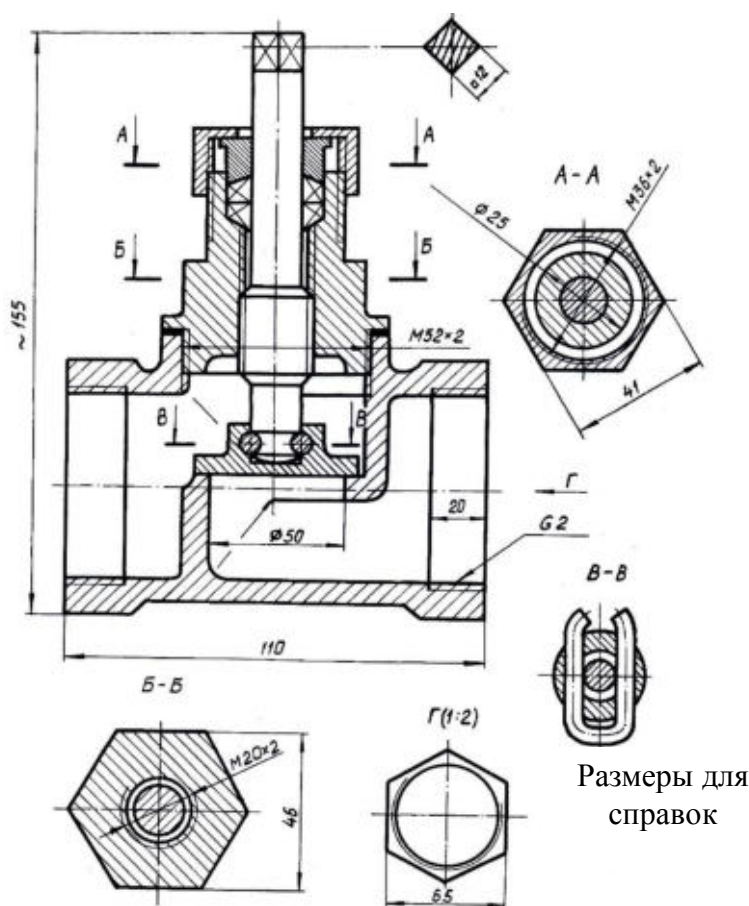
К построению изображений и нанесению размеров на сборочном чертеже «ВЕНТИЛЬ»
